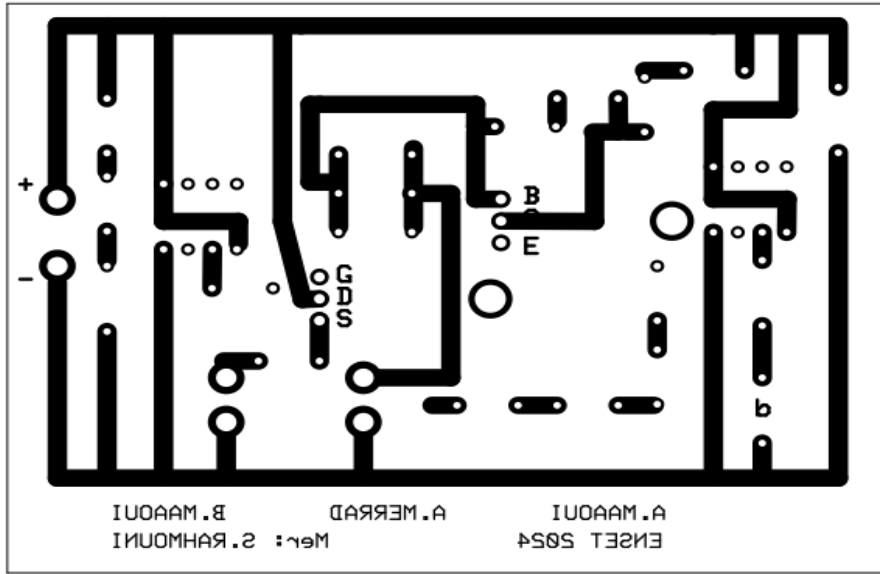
VI): تصميم الدارة بواسطة Express PCB.
